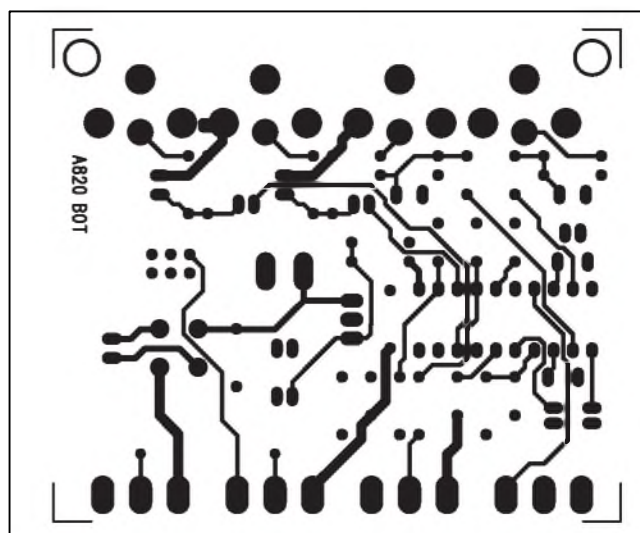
Obrazec desky spojů korekcí s obvodem LM1036 (strana BOTTOM)
